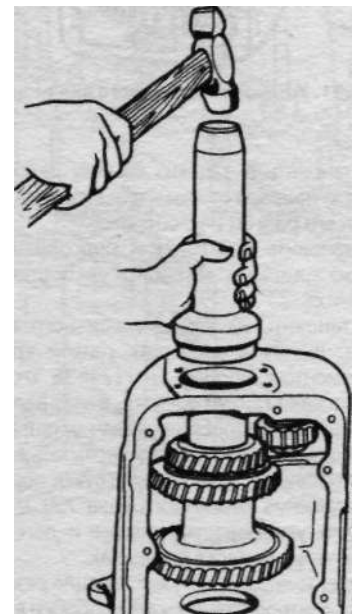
Запрессовка шарикового подшипника промежуточного вала
